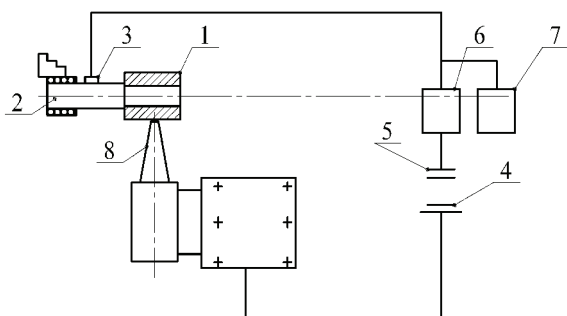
Схема вимірювання часу контакту інструмента з деталлю:
